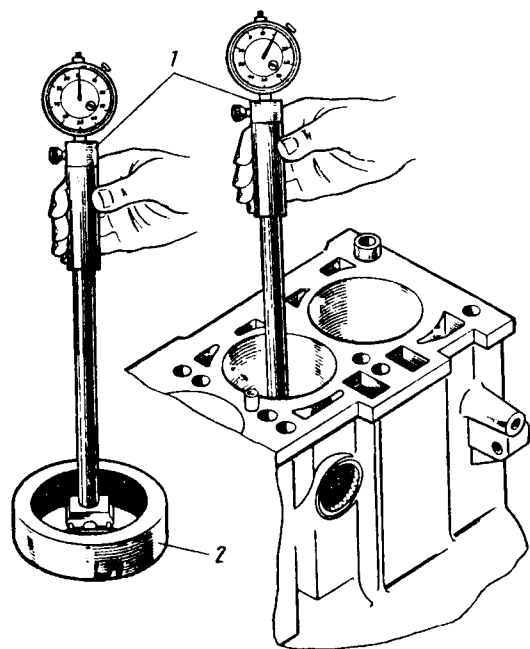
Замер диаметра цилиндра индикаторным нутромером:
